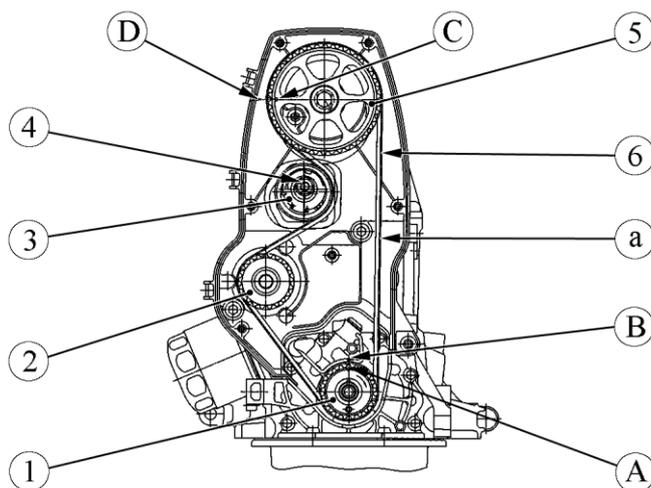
Детали привода распределительного вала двигателей 11186 и 21116:
